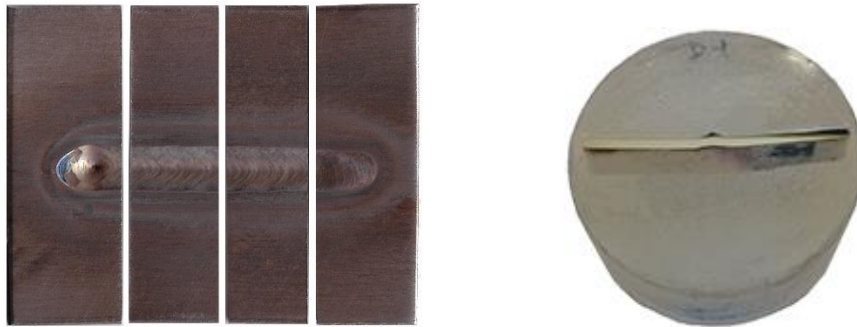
Esquema dos cortes das amostras soldadas em mm.
